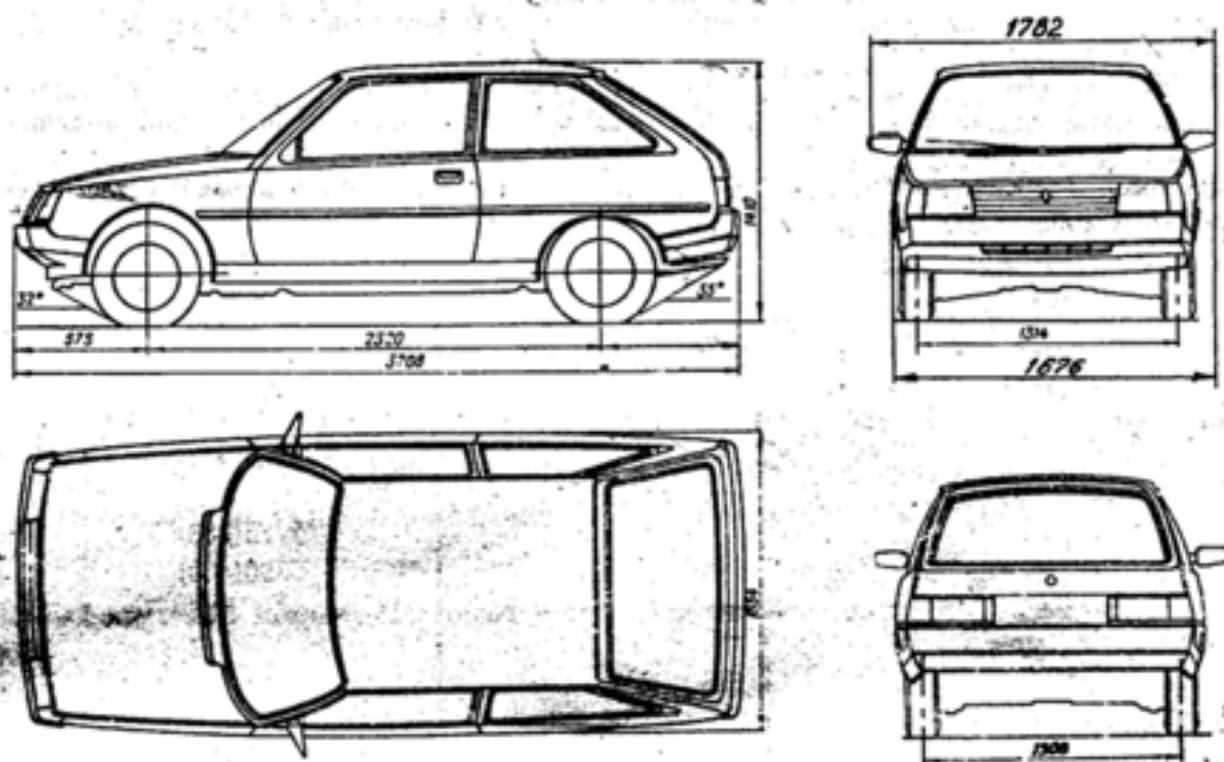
Основные габаритные размеры автомобилей ЗАЗ-110206, ЗАЗ-110216 (высота без нагрузки)
